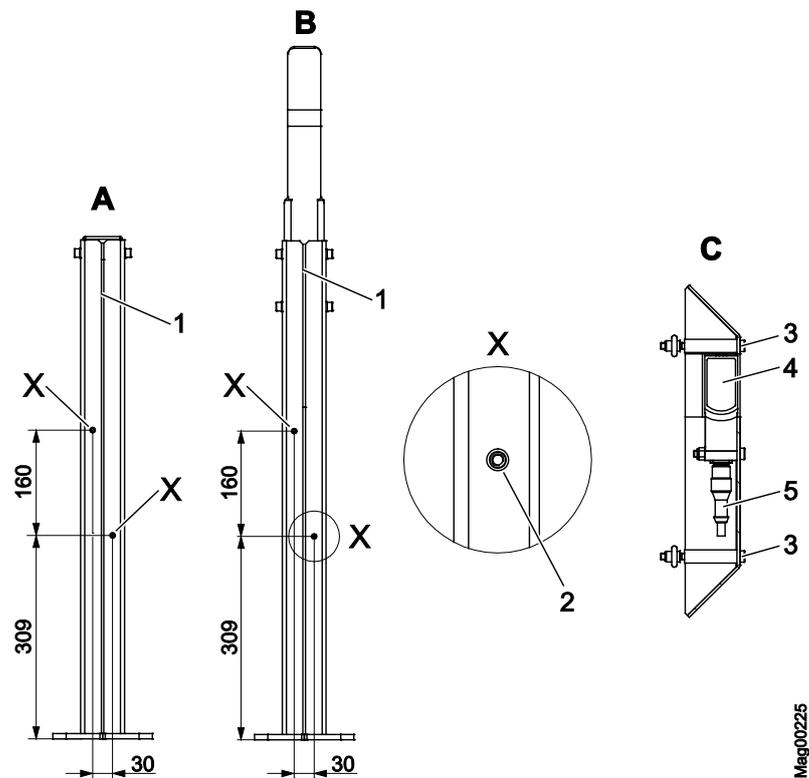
Монтаж корпуса фоторелейного барьера приемника на тумбе
